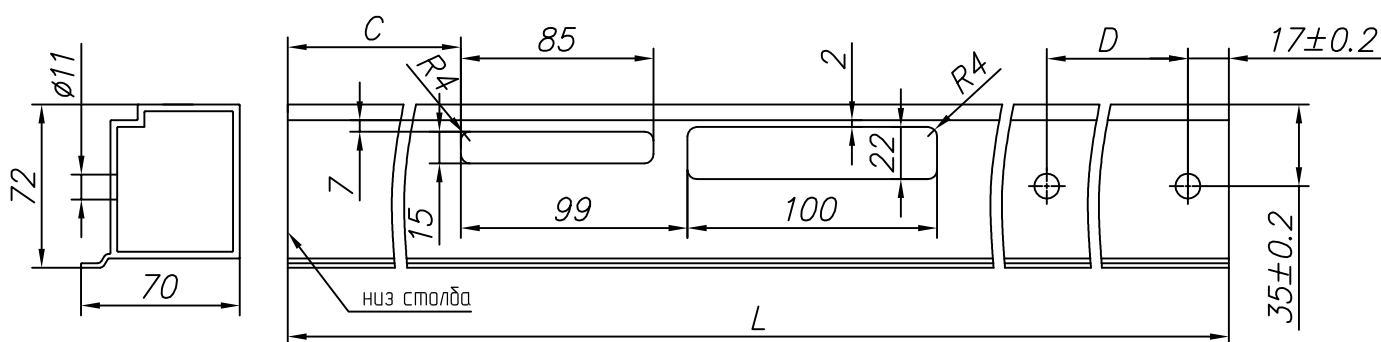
Изготовление столба притвора с пазом для автоматической защелки для калитки с правым открыванием (защелка 118WE)
